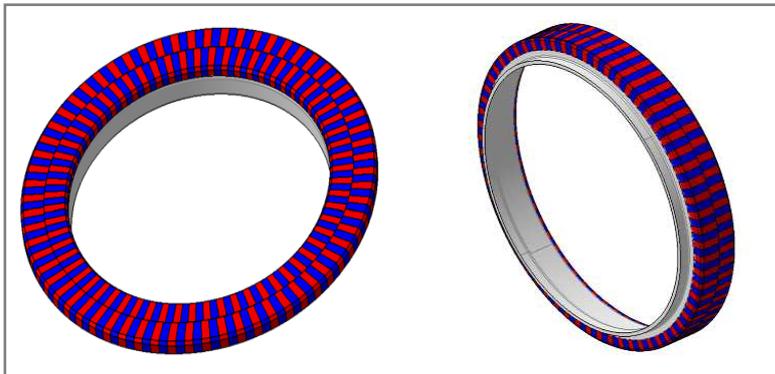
Technischer Aufbau - Die Magnetpaare sind zueinander versetzt, sodass der Sensor immer exakt erkennen kann, an welcher Stelle er sich befindet.
